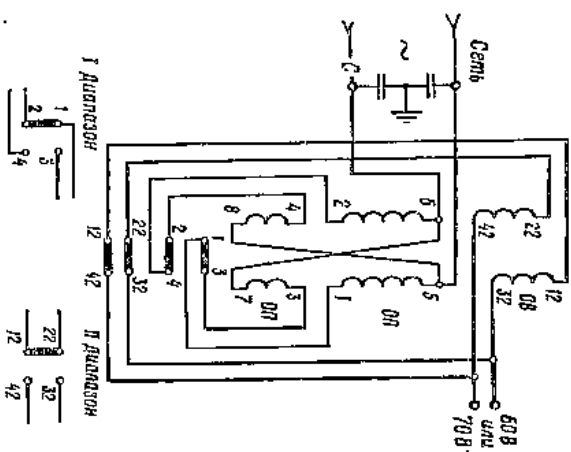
Схема сварочного трансформатора типа ТД-500
